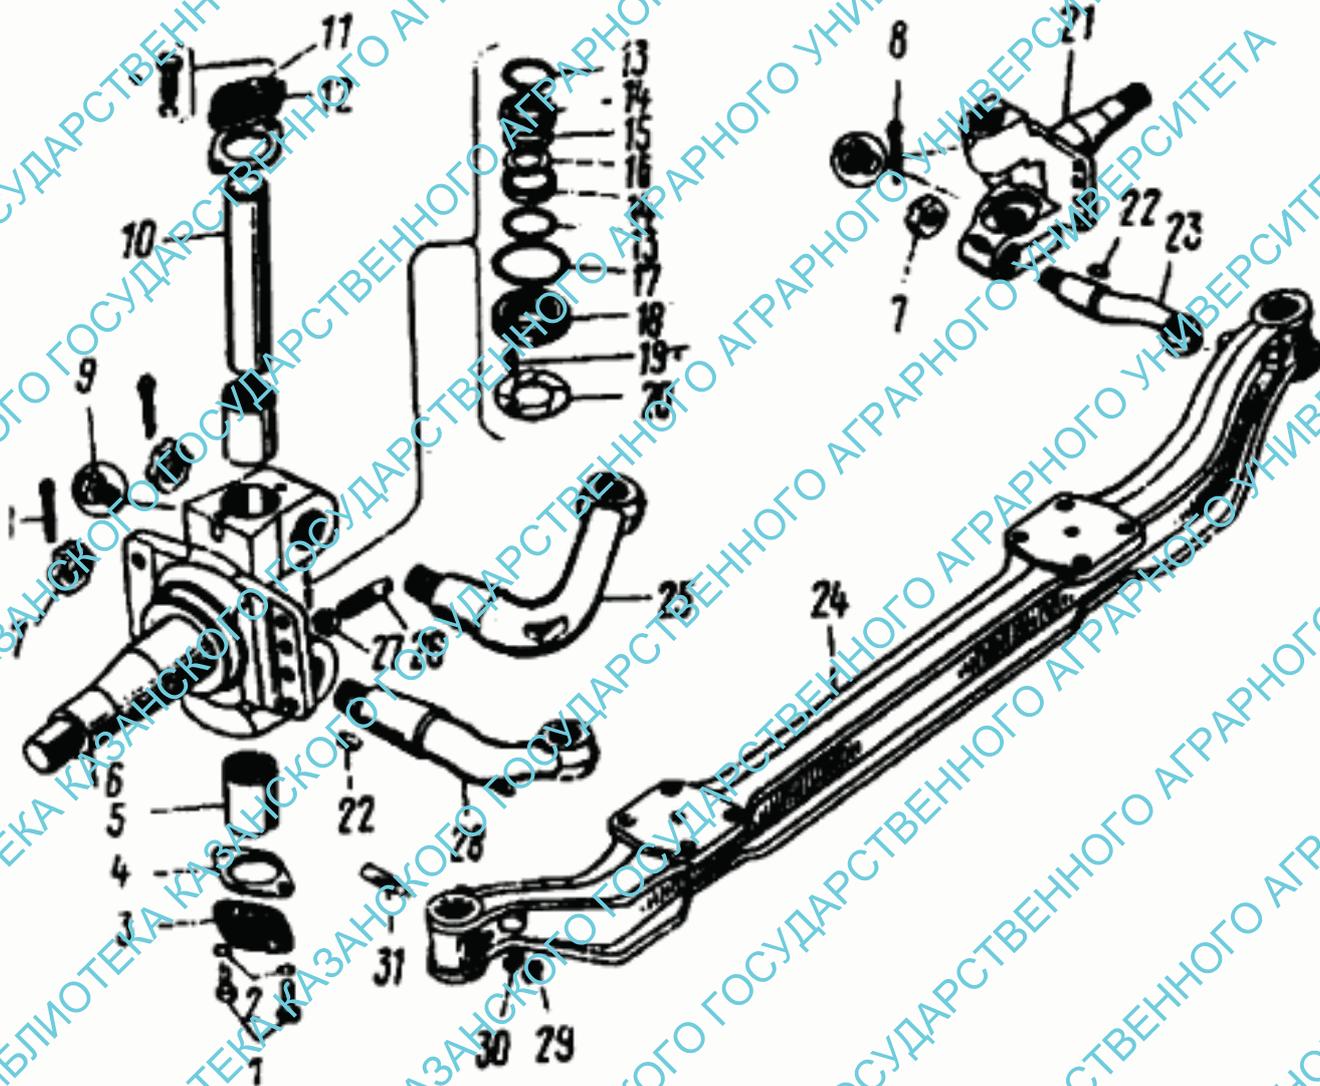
Передняя ось и поворотные кулаки: 1 - болт; 2, 30 - шайбы пружинные; 3 - крышка нижняя поворотного кулака; 4 - прокладка крышки; 5 - втулка шкворня; 6 - кулак левый поворотный переднего моста; 7, 27, 29 - гайки; 8 - шпилька разводной; 9 - масленка; 10 - шкворень; 11 - клапан предохранительный; 12 - крышка верхняя поворотного кулака; 13 - кольцо уплотнительное; 14 - обойма сальника; 15 - шайба кулака; 16 - шайба регулировочная; 17 - полукольцо сальника; 18 - кольцо опорного подшипника; 19 - штифт; 20 - шайба опорного подшипника; 21 - кулак правый
